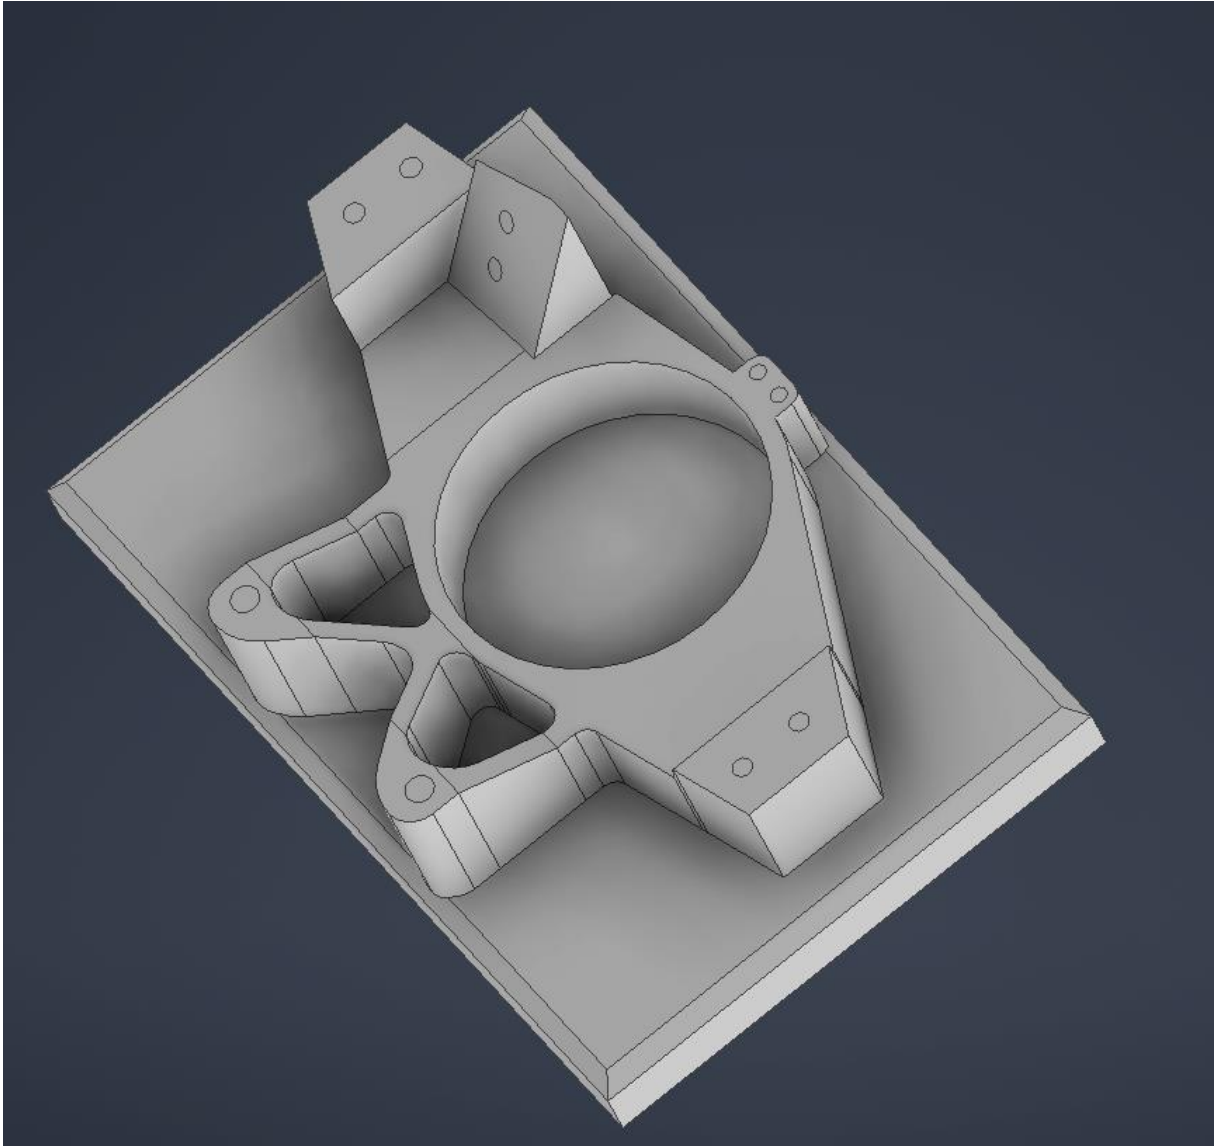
Simulering av spindel under svinging, med bolter.
